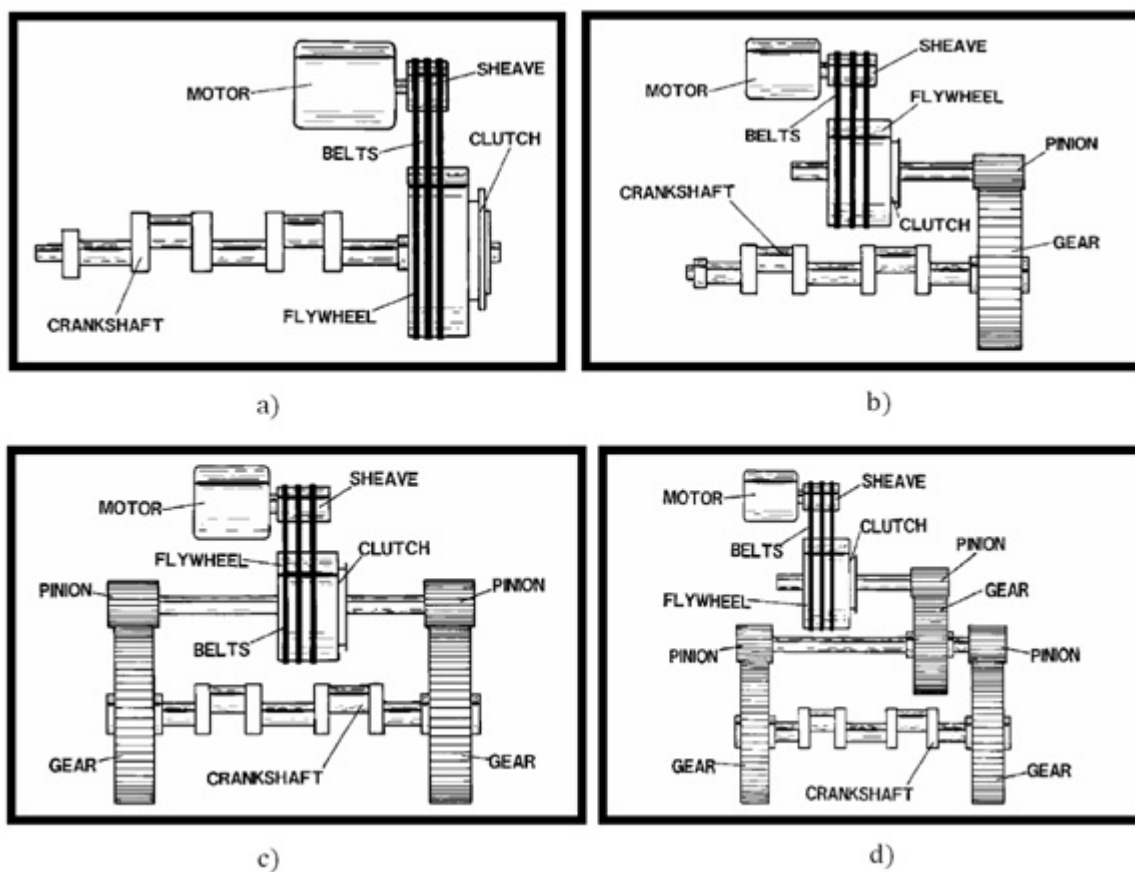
Transmissões: a) de ataque direto sem redução; b) com engrenagem redutora; c) conjugação de uma engrenagem redutora com uma gémea; d) conjugação de engrenagem redutora dupla com uma gémea [7]
